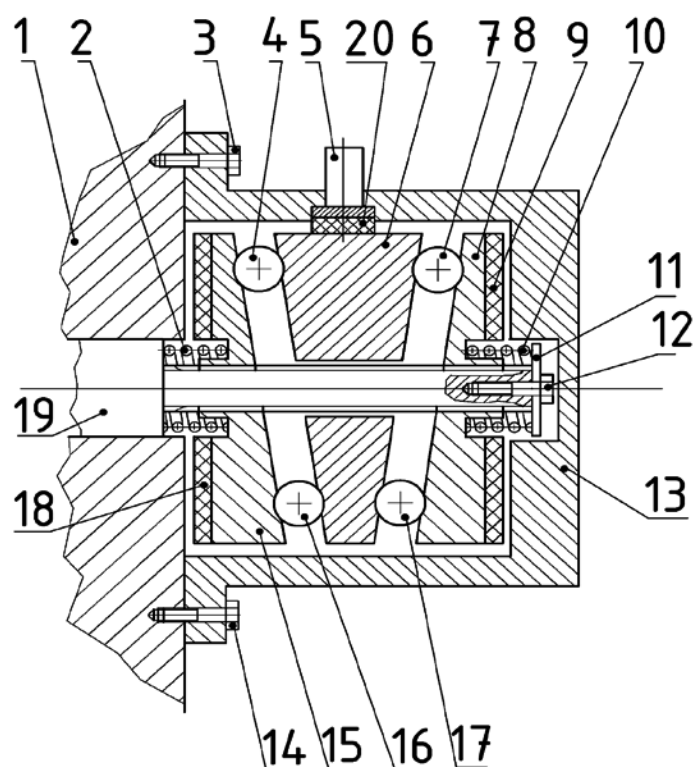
Тормозной механизм: 1 – корпус заднего моста; 2 – возвратная пружина левая; 3 – винт крепления крышки; 4 – шарики; 5 – шток; 6 – промежуточный диск; 7 – корпус тормоза; 8 – ведущая шестерня конечной передачи; 9 – фрикционная накладка; 10 – возвратная пружина правая; 11 – упорная шайба; 12 – винт крепления шайбы; 13 – кожух; 14 – винт крепления крышки; 15 – нажимной диск; 16 – шарик; 17 – шарик; 18 – фрикционная накладка; 19 – шлицевой вал; 20 – фрикционная накладка
